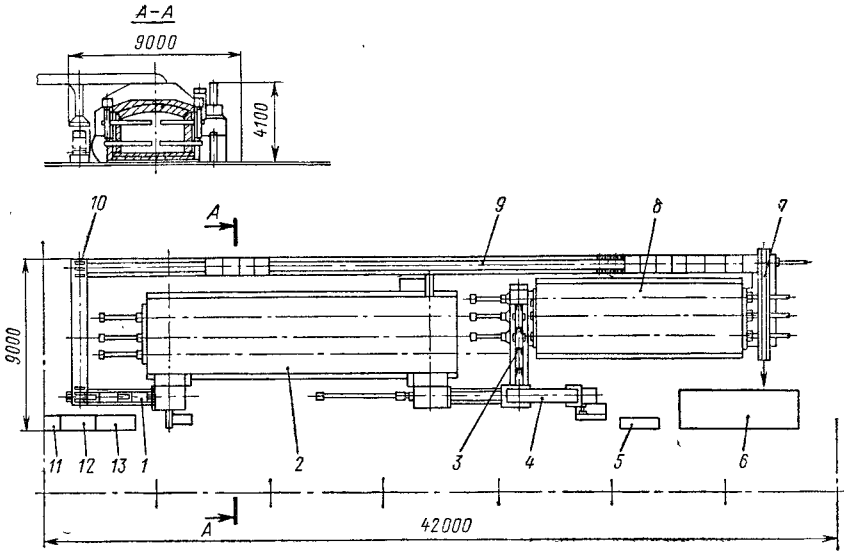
Агрегат для отжига отливок на ковкий чугун:
